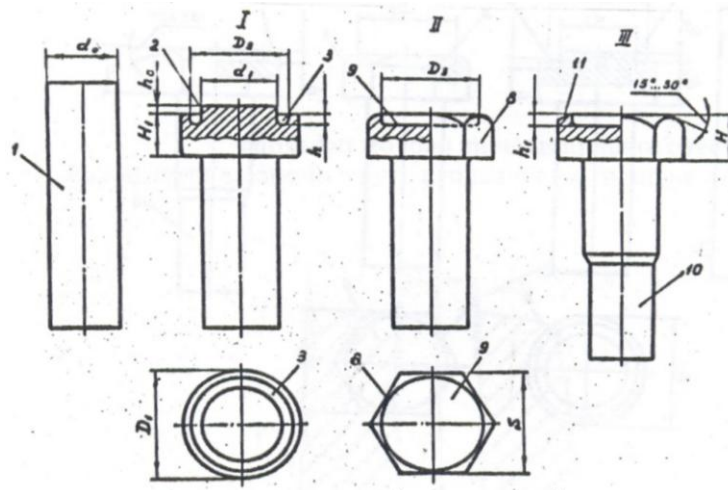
Схема процесса штамповки шестигранной головки с торцевой лункой
